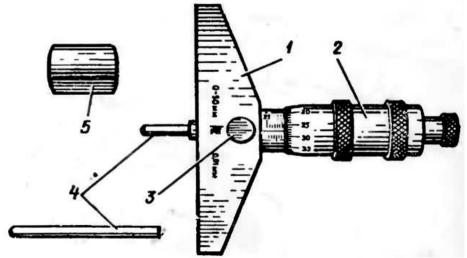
Общее устройство микрометрического глубиномера типа ГМ: 1- основание; 2- микрометрическая головка; 3- стопор; 4- сменные измерительные стержни ;5- установочная мера
